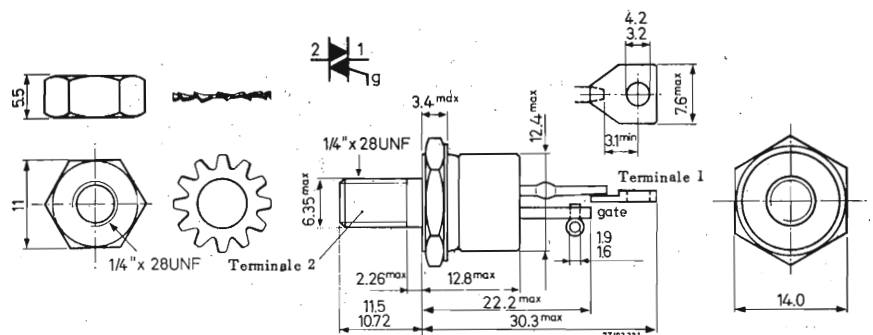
Disegno illustrante le dimensioni d'ingombro del triac BTX94/700 utilizzato nella costruzione di questo montaggio.
